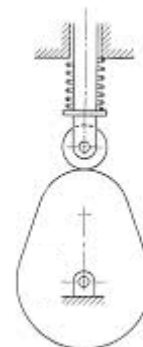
Nepředepnutý mechanismus Master-Slave
